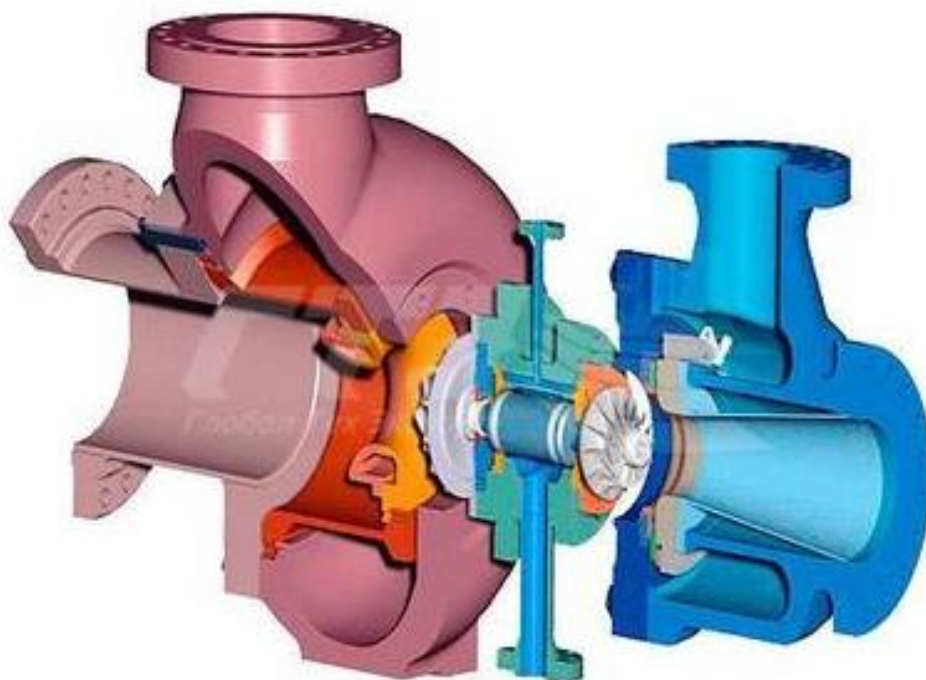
Общий вид турбодетандерного агрегата
